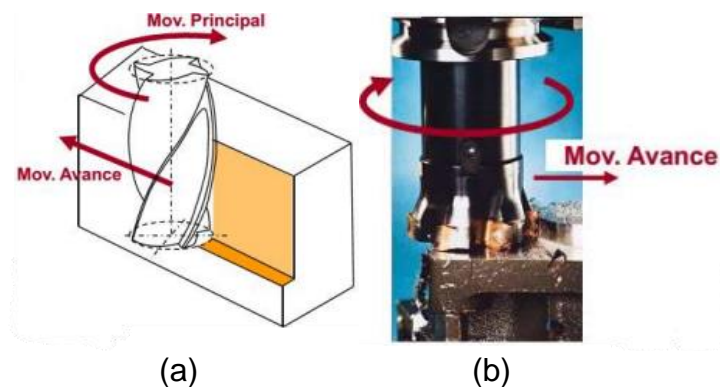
(a) y (b) Movimientos de corte y avance en una fresadora [9].
